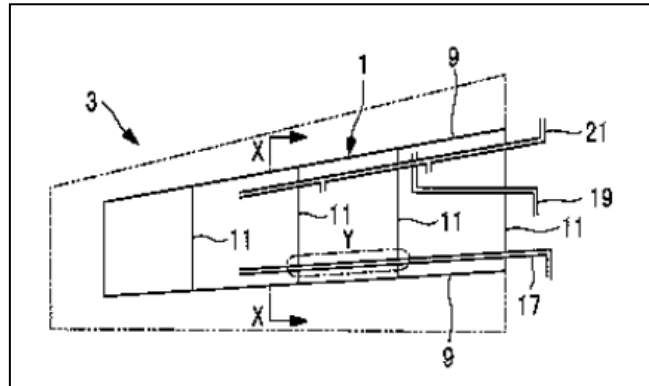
Sección en planta que representa esquemáticamente la vista de un depósito de combustible. Fuente: JP2010126133.
